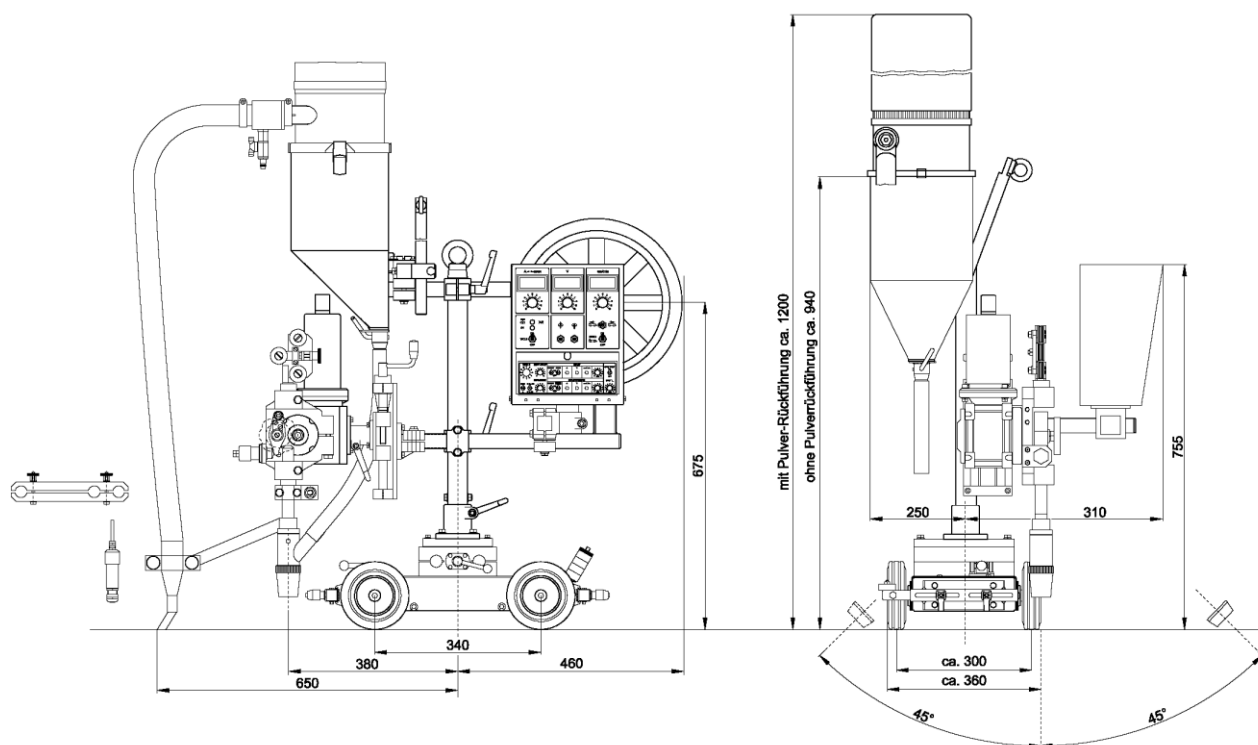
Автомат сварочный КА 2-UPP фирмы «EWM HighTec Welding GmbH»
